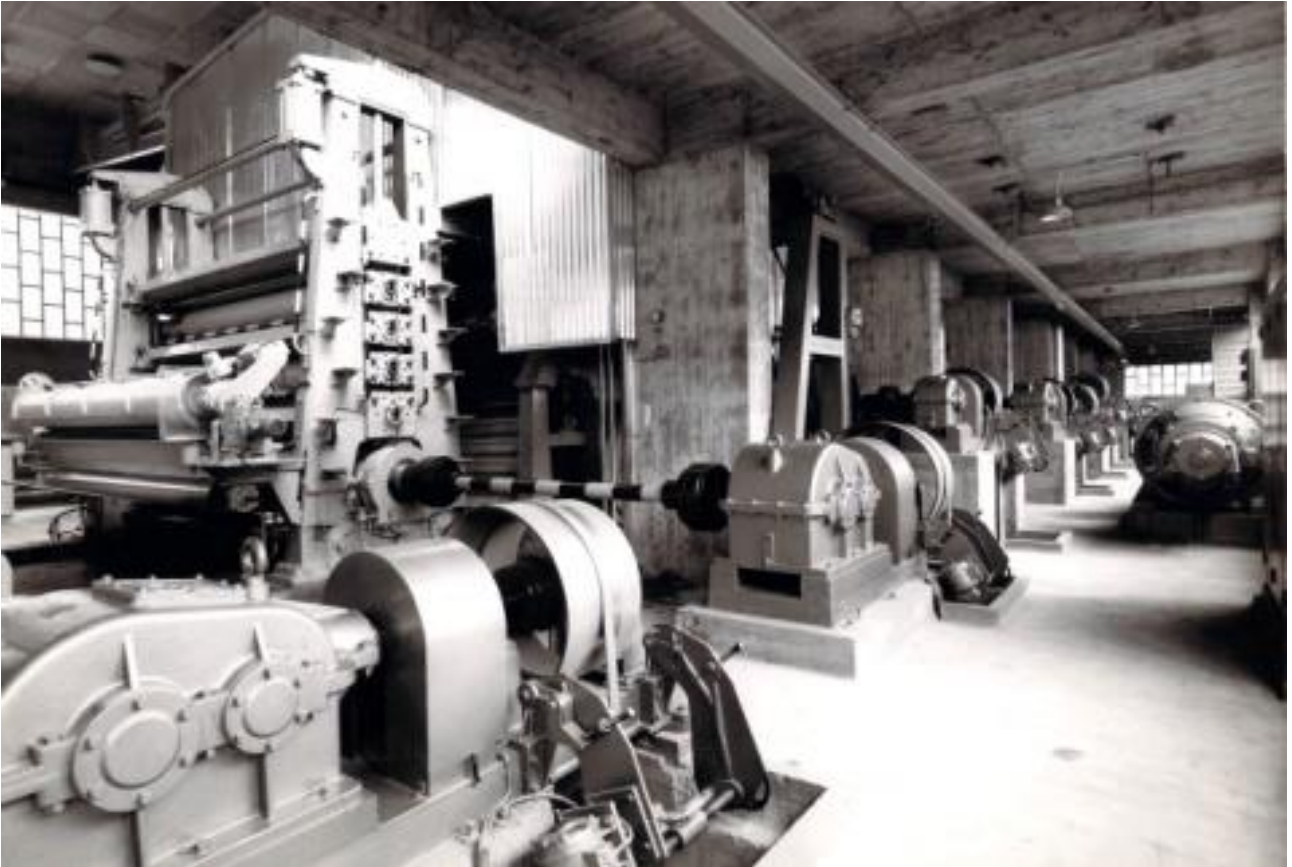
Ejes de accionamiento de cilindros de la máquina instalada al interior del pabellón de cubierta abovedada. (AEPE F 698)
